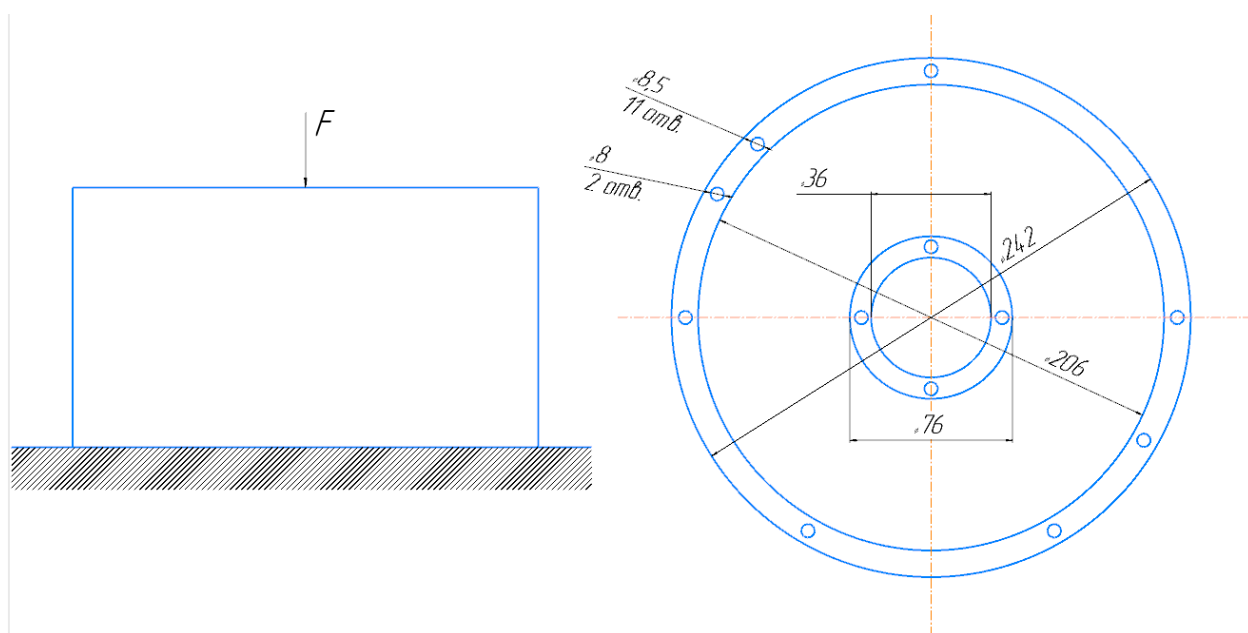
расчетная схема кольца и его поперечное сечение
